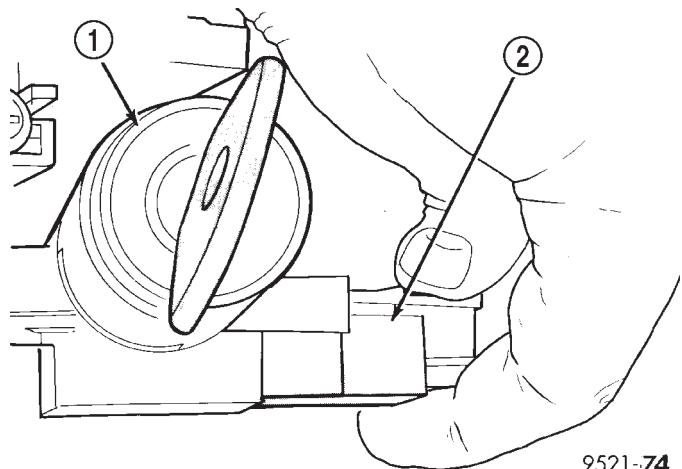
Cable de interbloqueo en la columna de dirección
